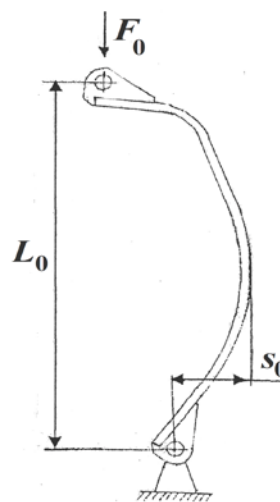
Схема нагружения упругого элемента в виде пластинчатой пружины (вид сбоку) без нагрузки (F_0): L_0 – размер пружины в продольном направлении, s_0 – в поперечном
